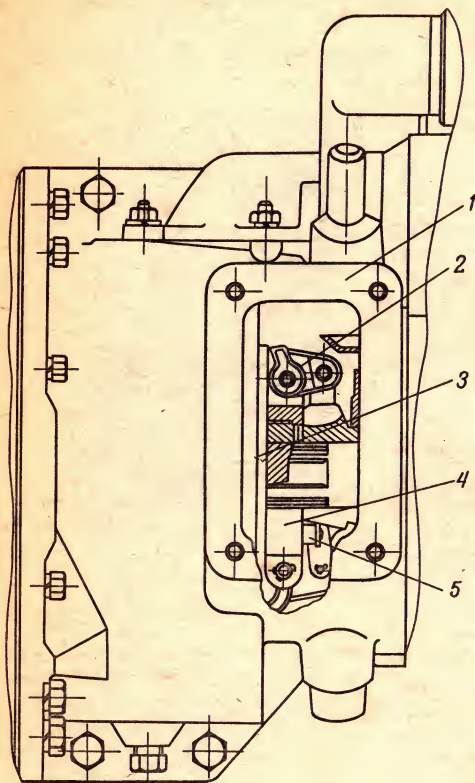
Муфта сцепления пускового устройства двигателя Д-130Т:
